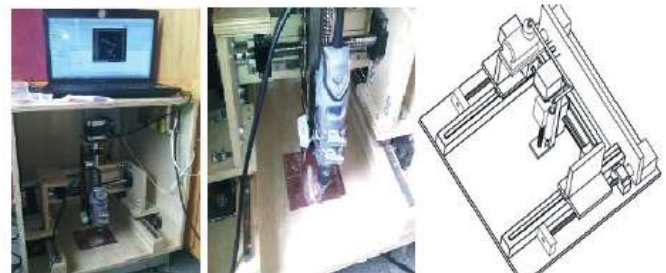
CNC realizando el calado en la PCB y Vista aérea de prototipo en formato CAD
